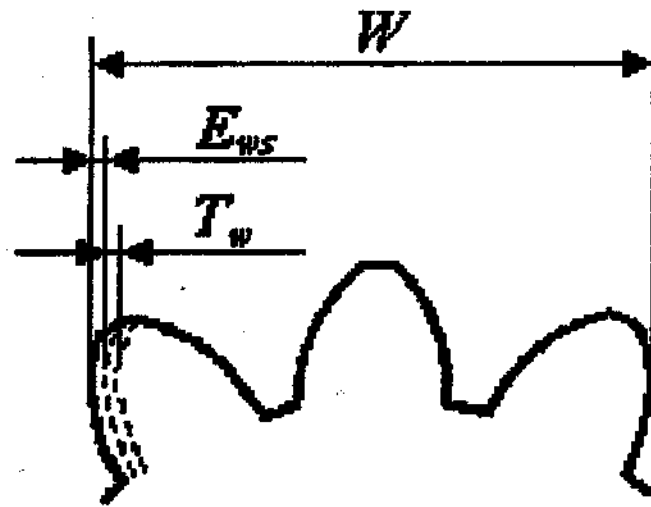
Общая нормаль профиля зубчатого колеса
